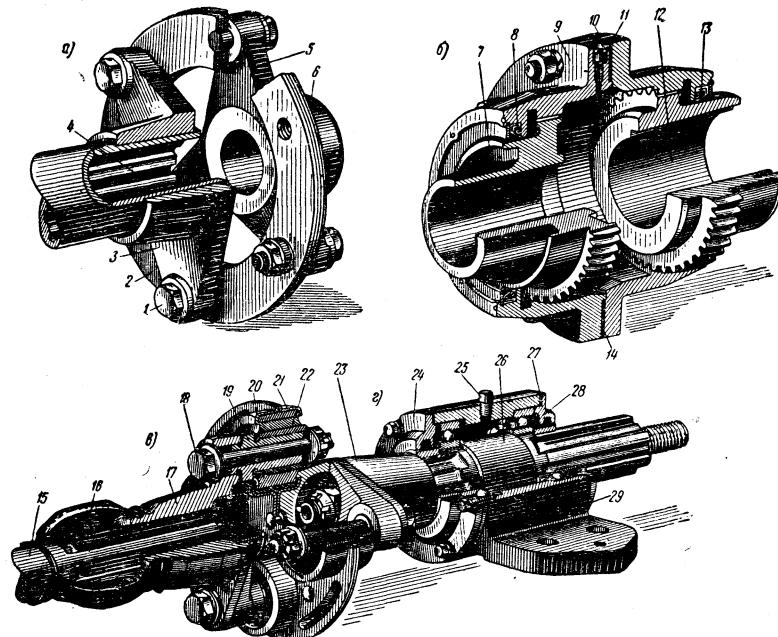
Соединительные муфты и опора подшипников привода вентилятора и компрессора на тепловозе ТЭЗ:
